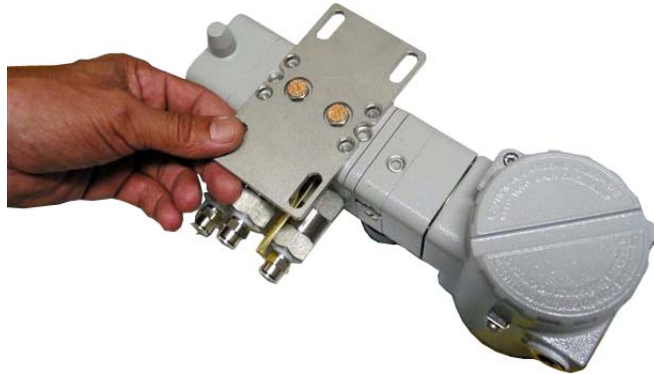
Chapa de Fixação sendo montada no Suporte
